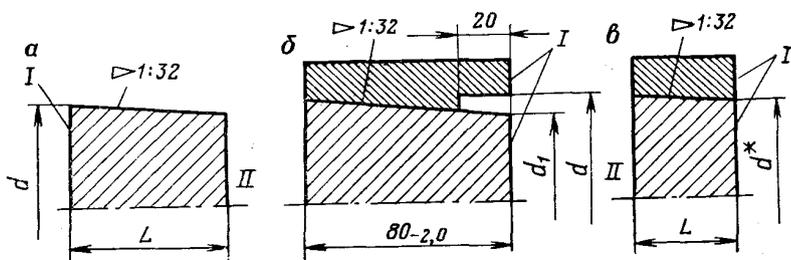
Гладкие калибры-пробки и калибры-кольца для контроля резьбы ТТ:
